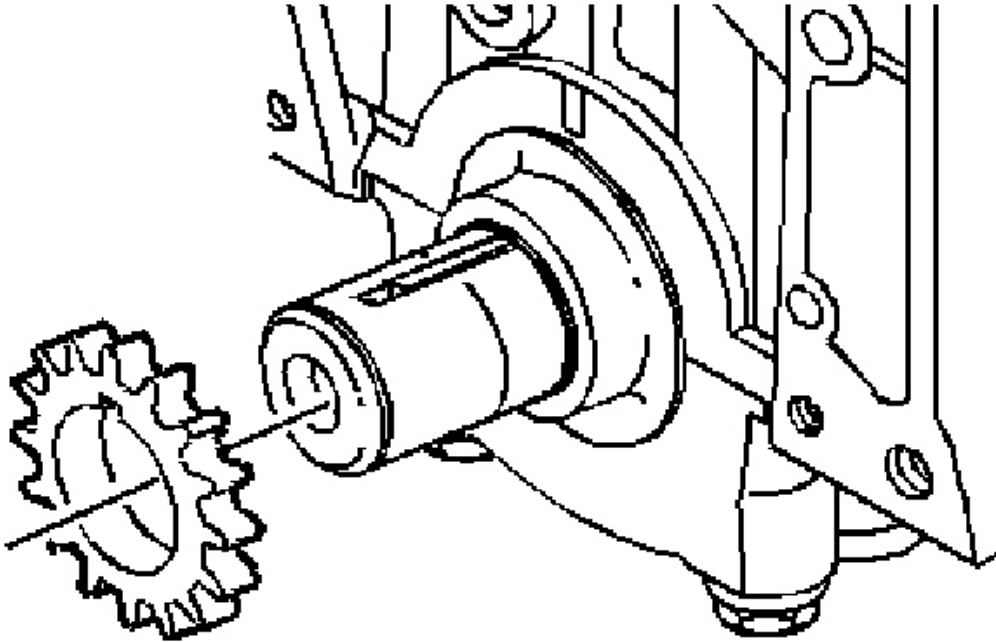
Vista de árbol de levas Cortesía del sensor de posición de la General Motors Corp.
